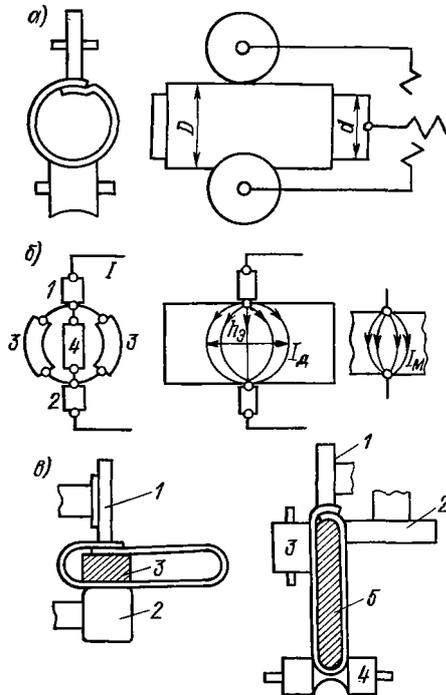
Технологические приемы сварки трубчатых элементов из тонколистового металла
